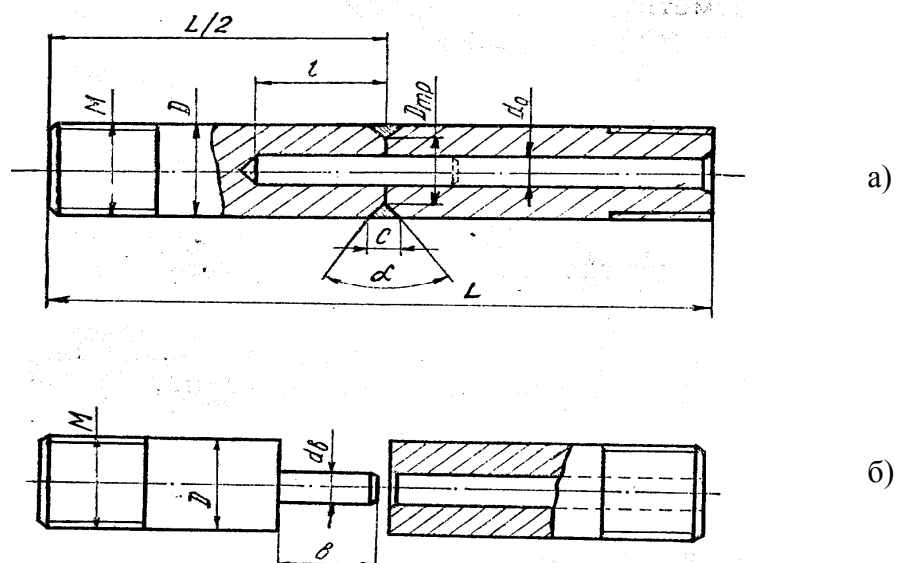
Складений трубчастий зразок з внутрішньою кільцевою тріщиною в наплавці – (а); ліва і права частини; зразка – (б)
